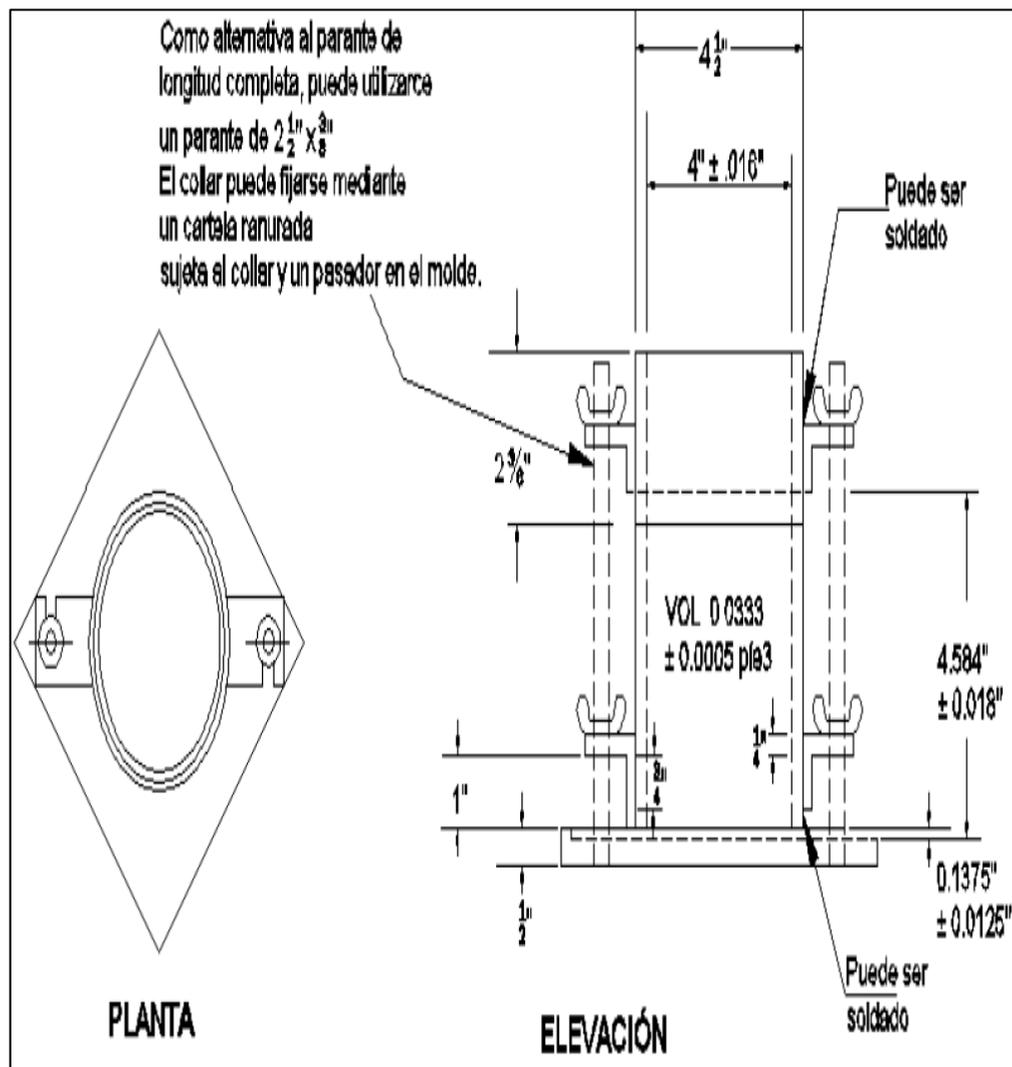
Molde cilíndrico de 4.0 pulgadas.
